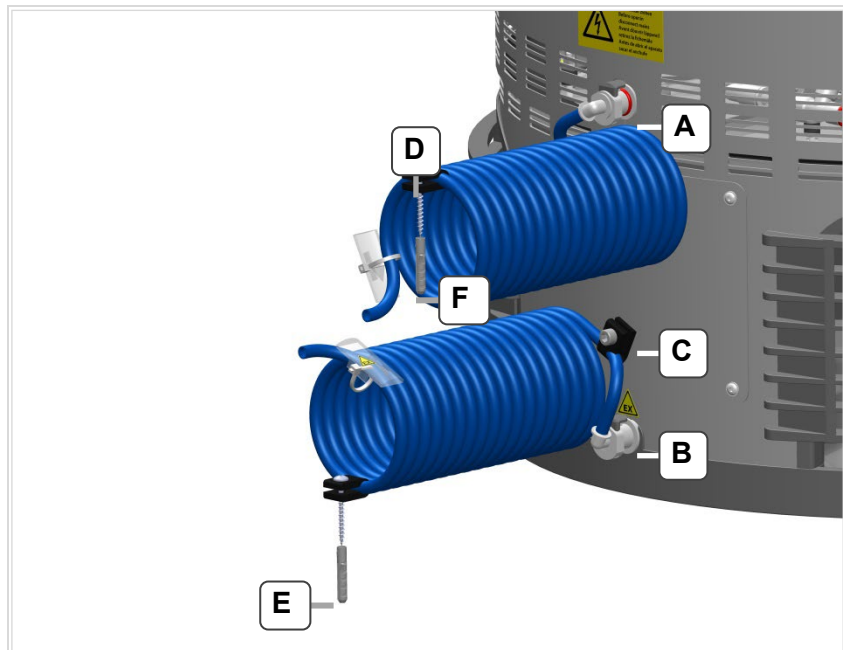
Be- und Entlüftungsanschlüsse mit Abluftschläuchen
